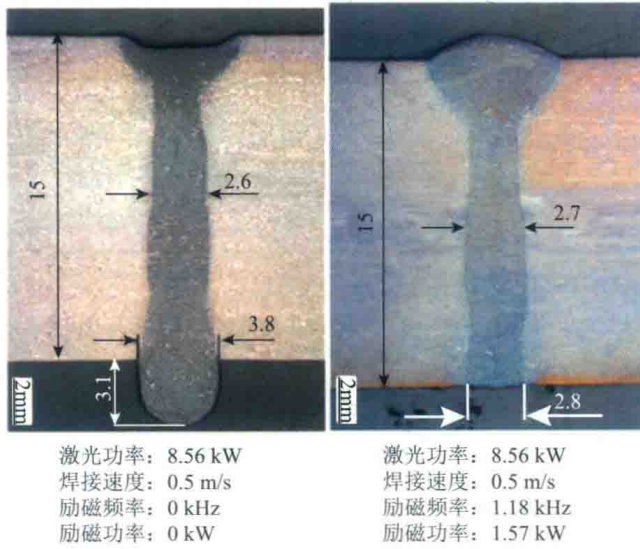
15mm 厚 2205 双相不锈钢焊缝截面形貌<sup>[12]</sup>
